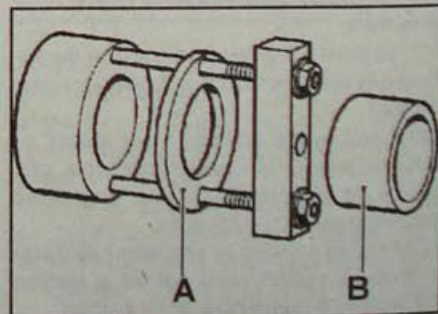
Приспособление Т.АВ. 1261-01 для установки шарового шарнира:
